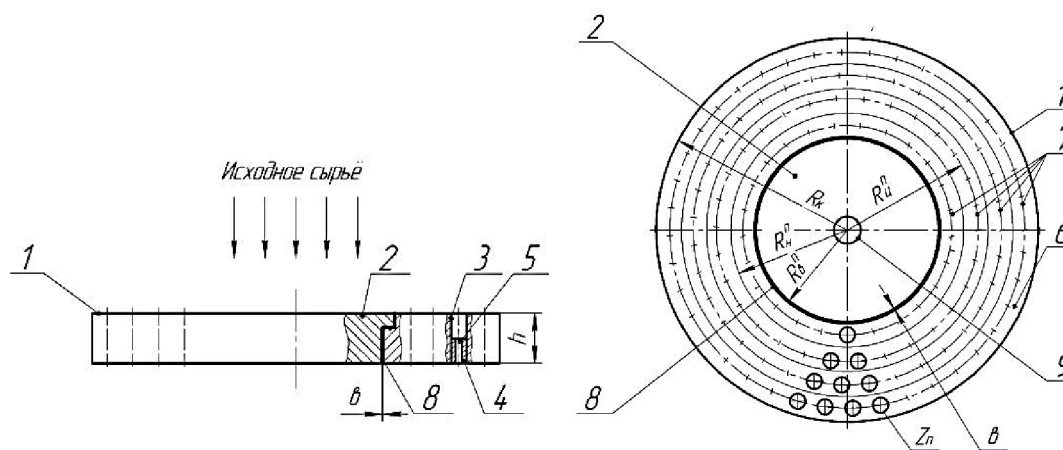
Принципиально-конструктивная схема составной матрицы для производства макаронных изделий: 1 – корпус матрицы; 2 – основание; 3 – колодцы; 4 – вкладыши; 5 – формующие отверстия; 6 – кольца условные; 7 – окружности цилиндрические; 8 – зазор; 9 – отверстие центральное; 10 – выступ; R_k – радиус корпуса матрицы; R_n^o – центральный радиус n -го условного кольца; R_n^i – наружный радиус n -го условного кольца; R_n^e – внутренний радиус n -го условного кольца; b – ширина зазора; Z_n – количество колодцев; h – высота (толщина) матрицы
